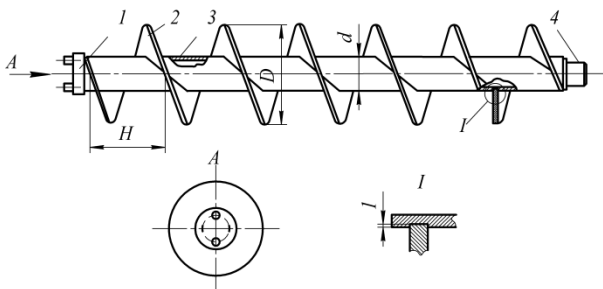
Шнек с полым валом: 1 – опорная цапфа; 2 – виток; 3 – полый вал; 4 – ведущая цапфа
